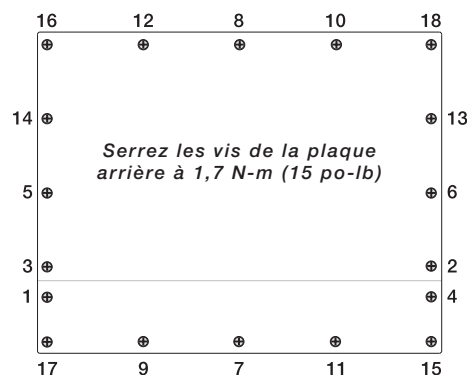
Plaque arrière du boîtier de l'indicateur 920i
